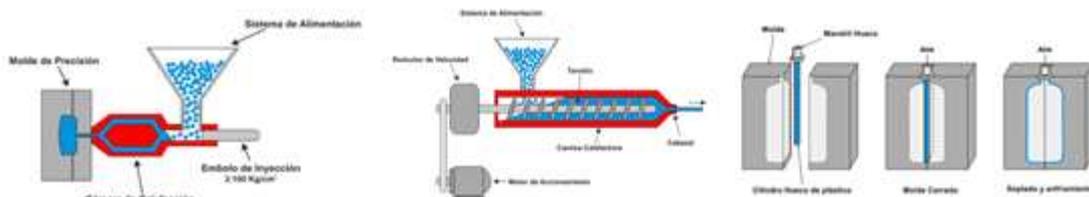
(a) Moldeo por inyección; (b) Moldeo por extrusión; (c) Moldeo por soplado
